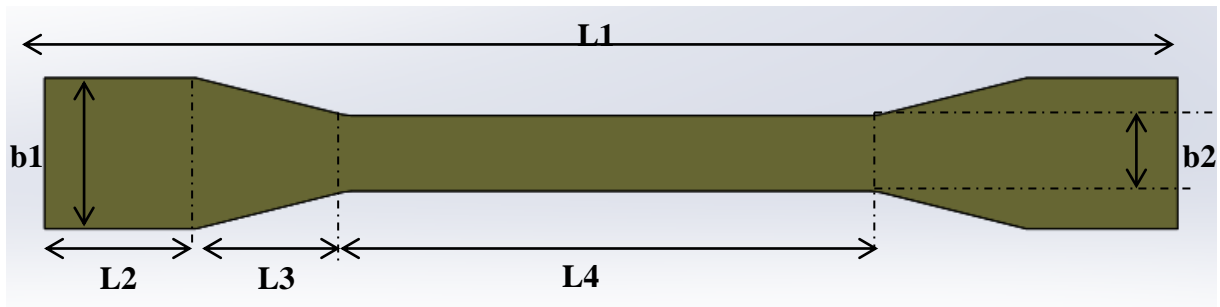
Géométrie des éprouvettes pour la traction des matrices époxydes
